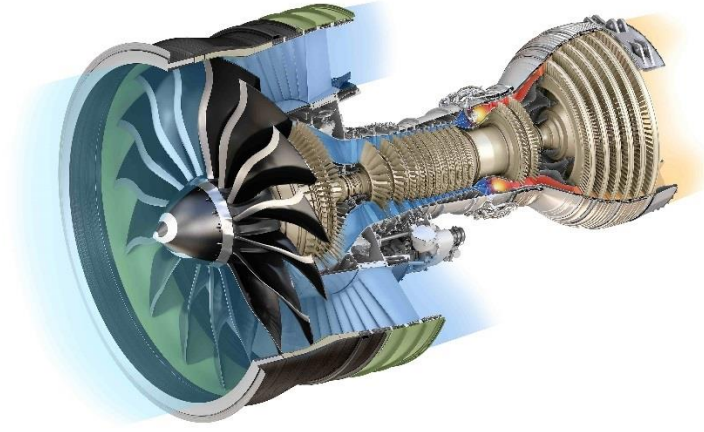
Bir turbofan motorunun iç kısmındaki komponentler [20]
